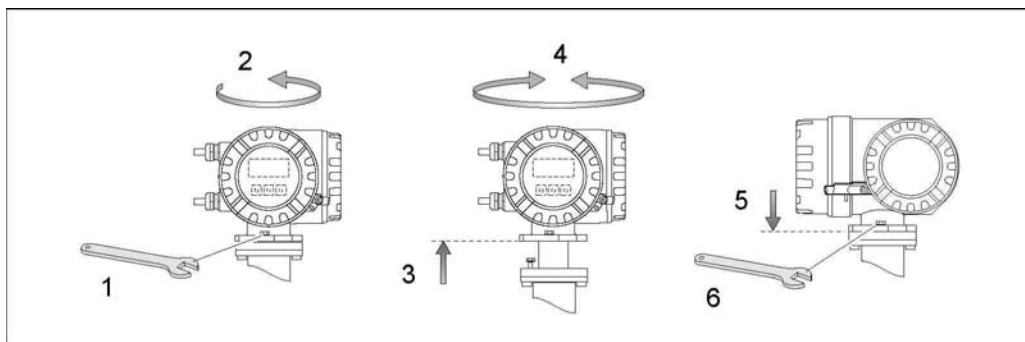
Вращение корпуса трансмиттера (алюминиевый полевой корпус)
